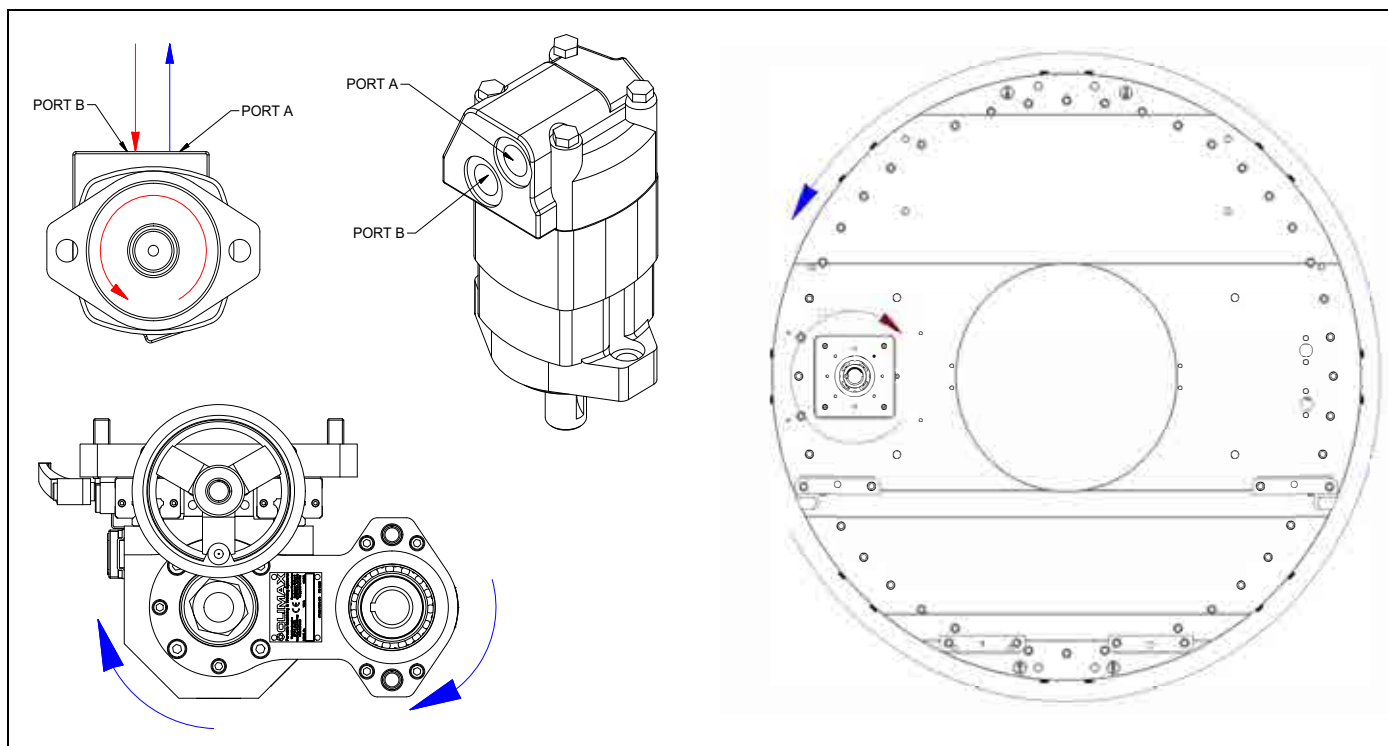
Направление вращения гидравлического двигателя, поворотного стола и фрезерной головки
